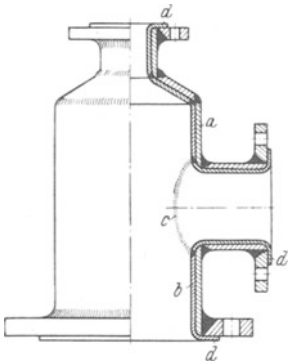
Schweißung eines innen mit nichtrostendem Stahl ausgekleideten Behälters.
